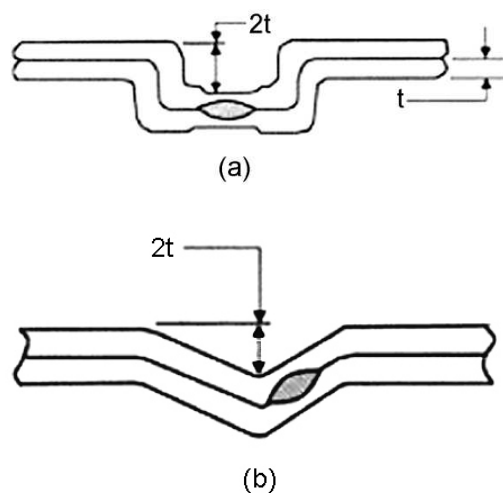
21. Distorsiones producidas durante la soldadura
